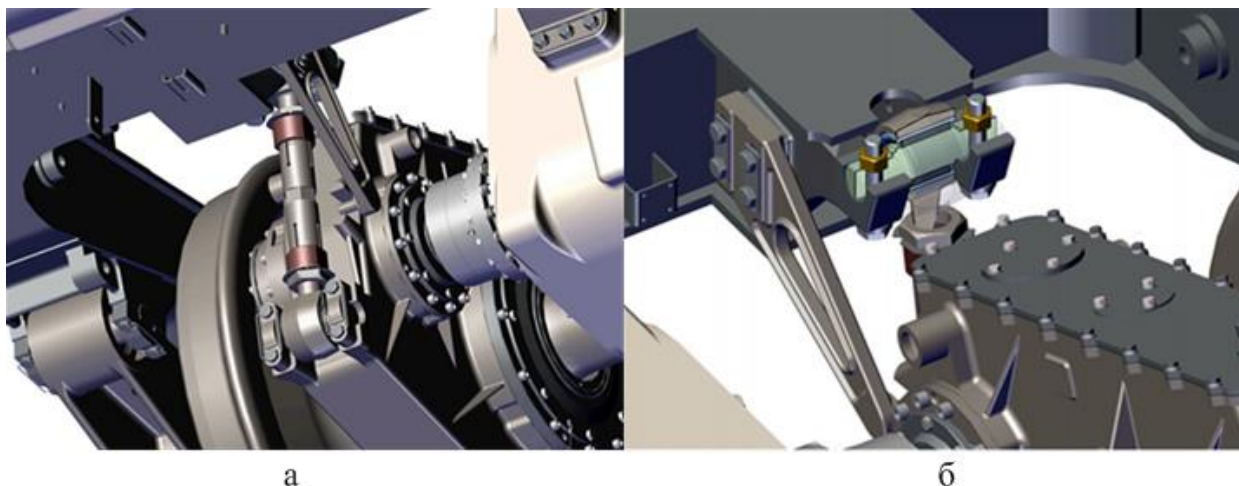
Візок вагона: а - кріплення редуктора до центральної балки; б - підвіска редуктора
